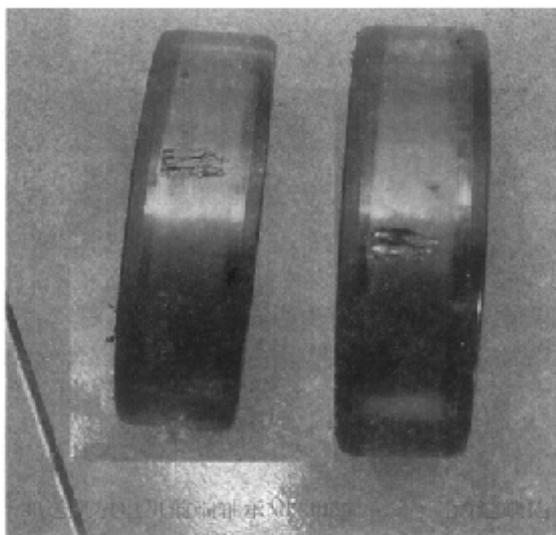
3A 轴流风机电机前端轴承缺陷
